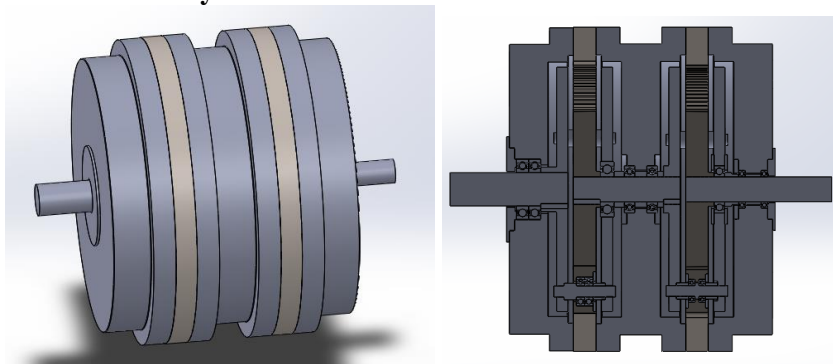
3D Poros & Sun Gear Transmisi 2
